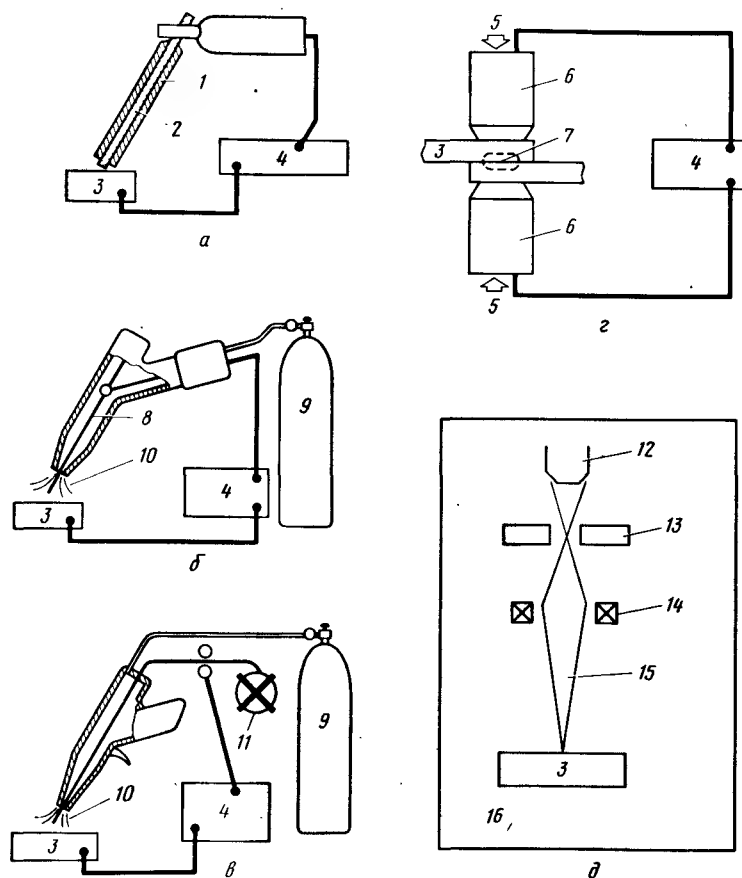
Несколько распространенных процессов сварки для соединения деталей из суперсплавов:
